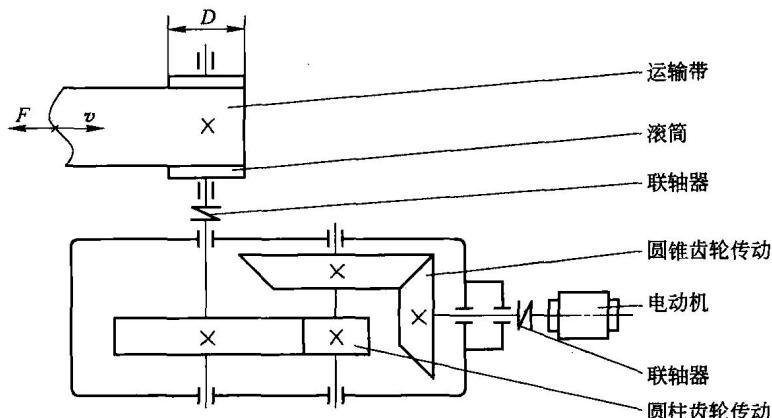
圆锥 - 圆柱二级齿轮减速器组成的带式运输机
